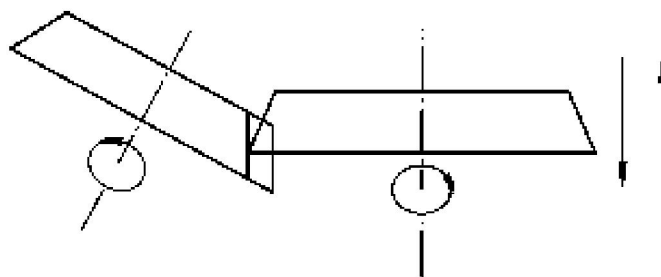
Схема обработки неэвольвентного конического колеса цилиндрической передачи
